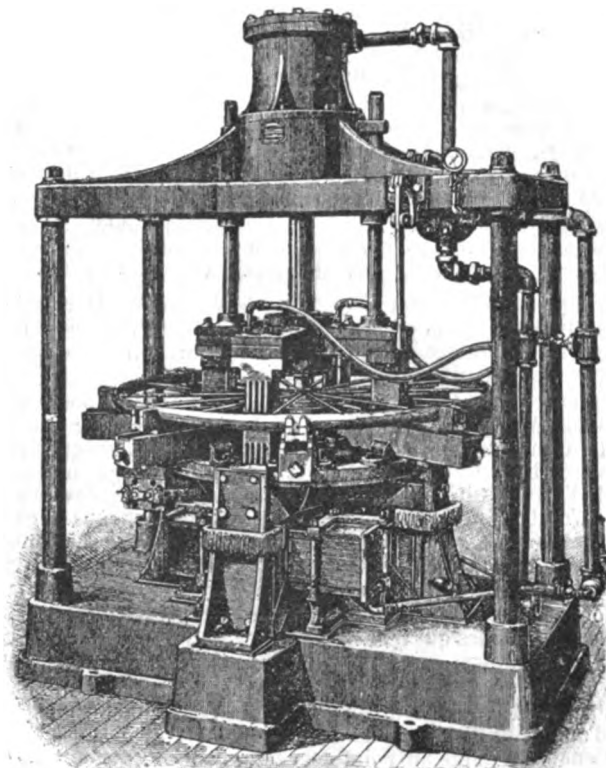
Vue d'ensemble de la nouvelle presse électrique à souder.
